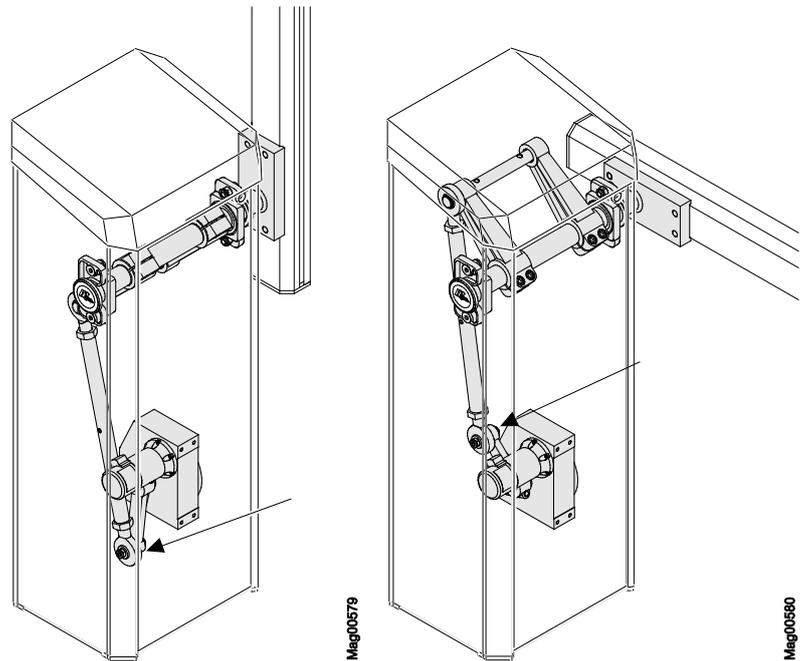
Access XL2, Schrankenbaum manuell schließen oder öffnen
